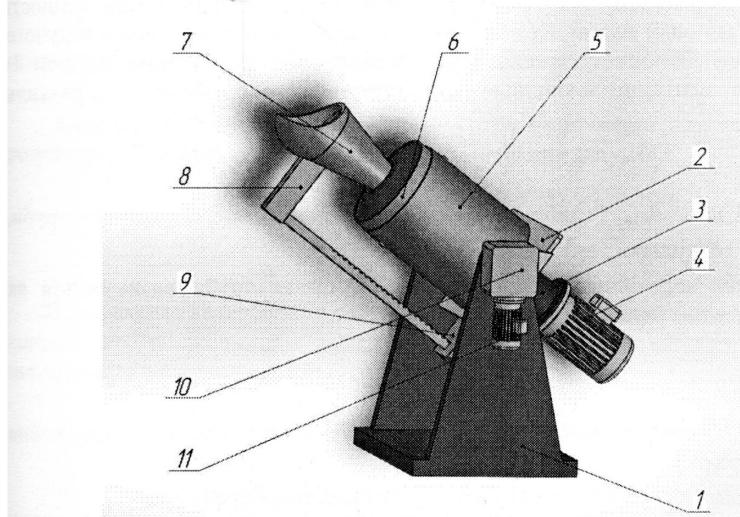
Конструкція установки відцентрового литва та армування заготовок
